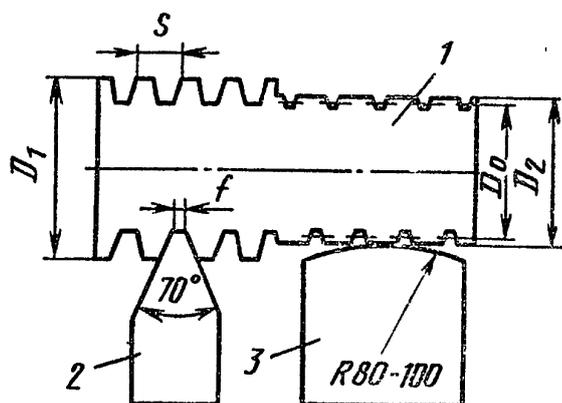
Схема электромеханической высадки и сглаживания деталей при ремонте неподвижных сопряжений: 1 – деталь; 2 – высаживающая пластина; 3 – сглаживающая пластина;  $D_0$  – диаметр изношенной детали;  $D_1$  – диаметр детали после высадки;  $D_2$  – диаметр детали после сглаживания
